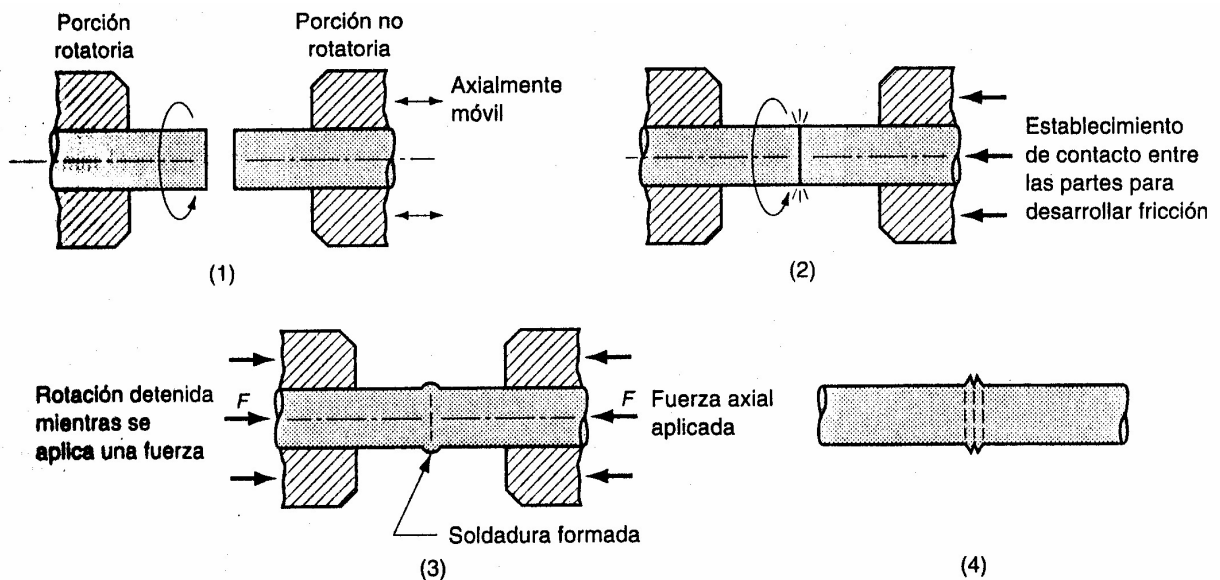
Soldadura por fricción (FRW) parte rotatoria, sin contacto; (2) establecimiento de contacto entre las partes para generar calor por fricción; (3) rotación detenida y presión axial aplicada; y (4) soldadura creada.
